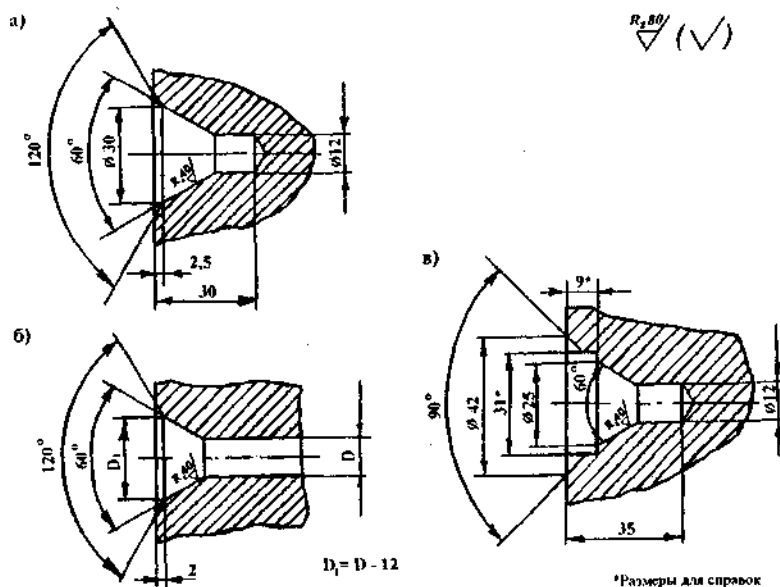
Отверстия центровые для осей: а — несверленных; б — сверленных; в — с торцевым креплением подшипников гайкой
